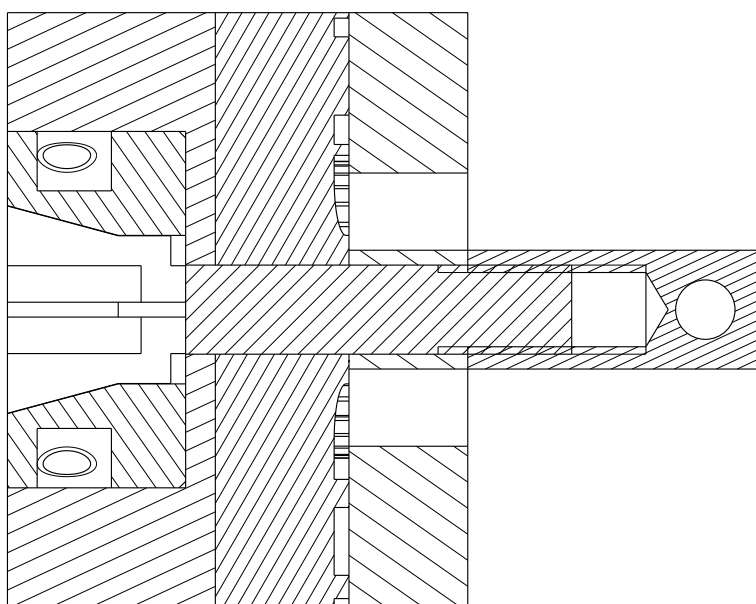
Rotoraufbau (Längsschnitt) mit 3D-gedrucktem Rotorelement *3D_A* (35 Schaufeln; Schaufelhöhe: 0,5 mm).
